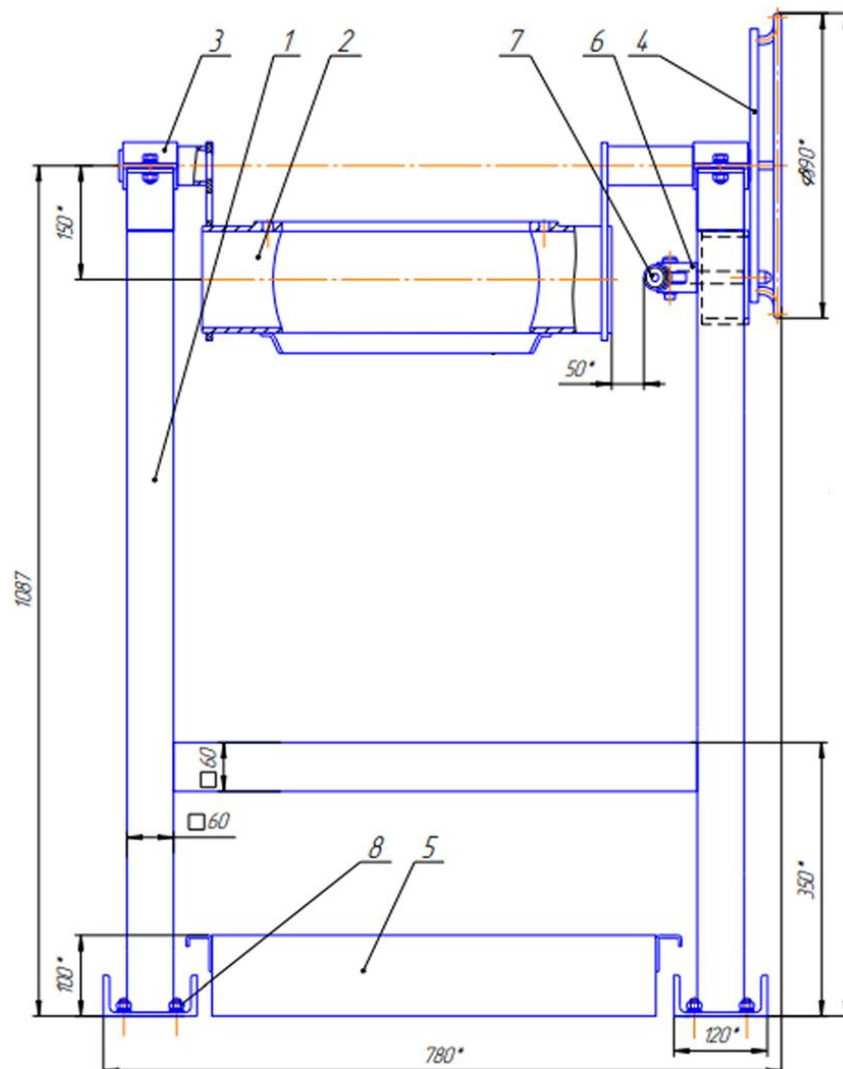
Стенд для ремонту редуктора заднього моста: 1 - рама, 2 - вісь, 3 - опора повороту осі, 4 - колесо, 5 - маслосбірний піддон, 6 - запірний механізм, 7 - виліт, 8 – якір
